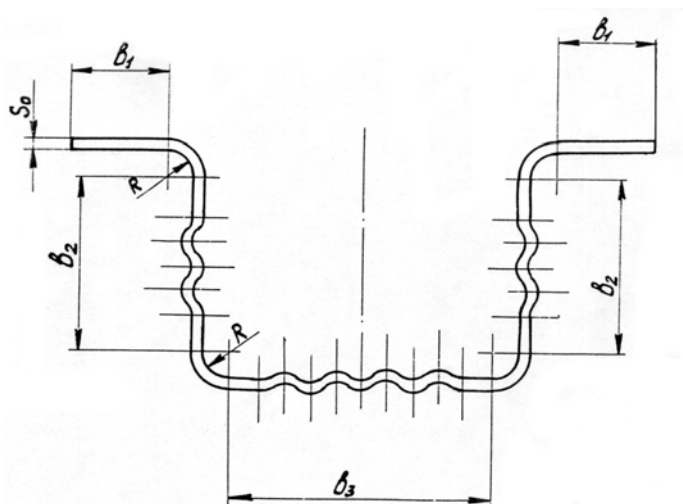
Схема для определения ширины исходной при формовке корытного профиля 80x60x32x2,5, мм.
